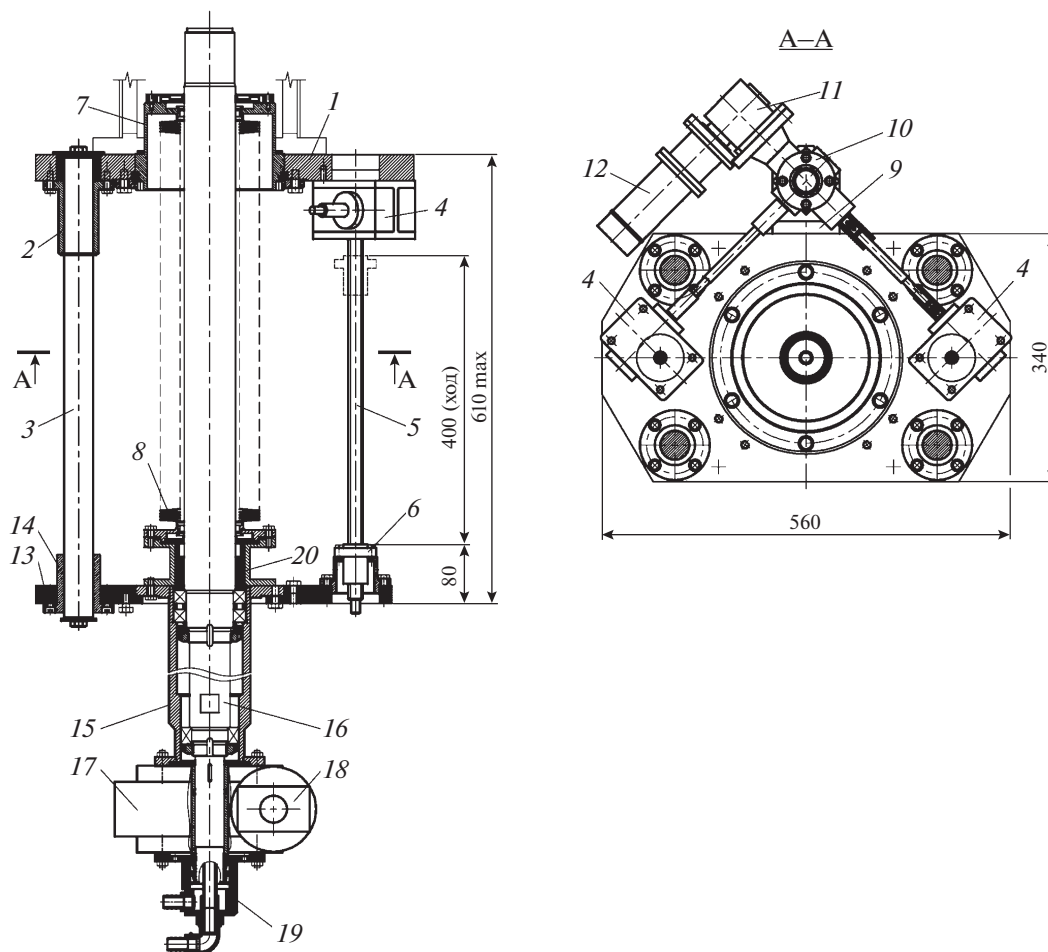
Привод для передачи вращательного и поступательного движения в вакуум. 1 — неподвижная плита; 2 — втулка; 3 — направляющие; 4 — редукторы; 5 — винты; 6 — гайки; 7 — корпус; 8 — сильфон; 9 — кронштейн; 10 — распределительное устройство; 11, 17 — червячные редукторы; 12, 18 — серводвигатели; 13 — подвижная плита; 14 — шариковая втулка; 15 — корпус; 16 — водоохлаждаемый шток; 19 — узел подачи воды; 20 — вакуумный ввод. Размеры даны в миллиметрах.
